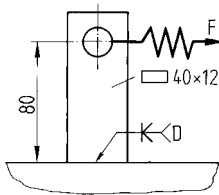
Schweißverbindung eines Flachstahls für Zugfederaufnahme
